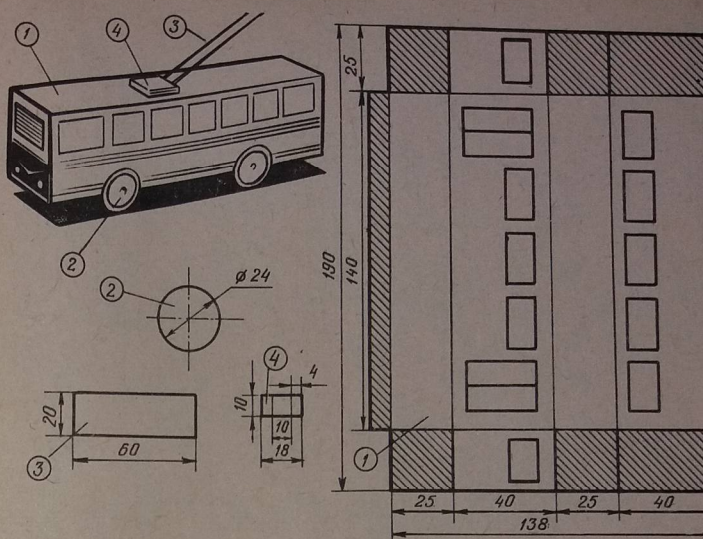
Модель троллейбуса: 1—развертка кузова; 2—колесо; 3—заготовка для штанги; 4—кронштейн
